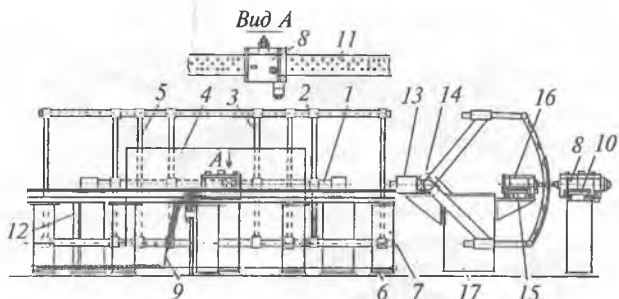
Установка СЗУ-Ф1 для сверления и зенкования отверстий в панелях одинарной кривизны: 1 — вал; 2 — рама; 3 — стойка; 4 — панель; 5 — ложемент; 6 — трос; 7 — колонна; 8 — агрегат СЗА-02; 9 — шланг; 10, 15 — направляющие с копир-шаблоном; 11 — копир-шаблон; 12 — блок программного управления; 13 — противовес; 14 — привод поддерживающего устройства; 16 — упорная головка; 17 — колонна
